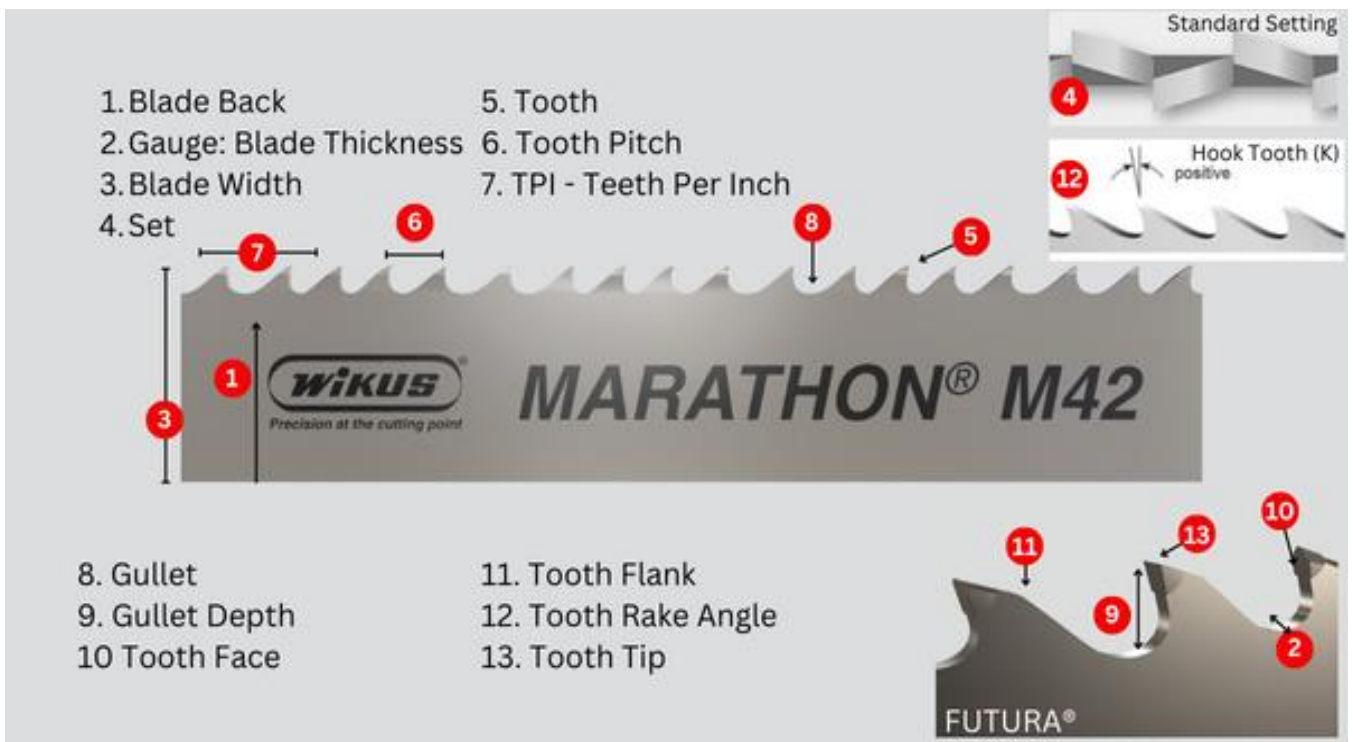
Основні елементи пильного полотна стрічкової пили.
